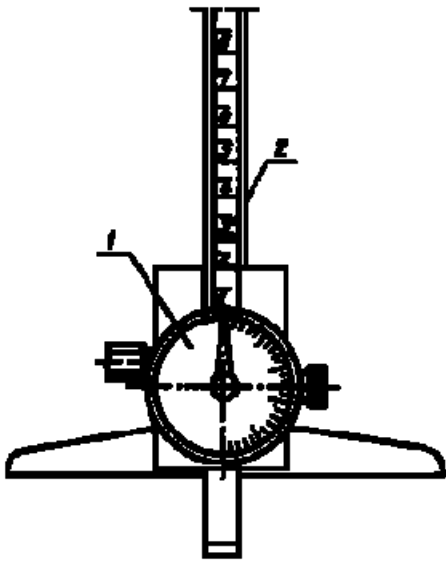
Штангенглубиномер типа ШГК: 1 – круговая шкала отсчетного устройства; 2 – штанга
